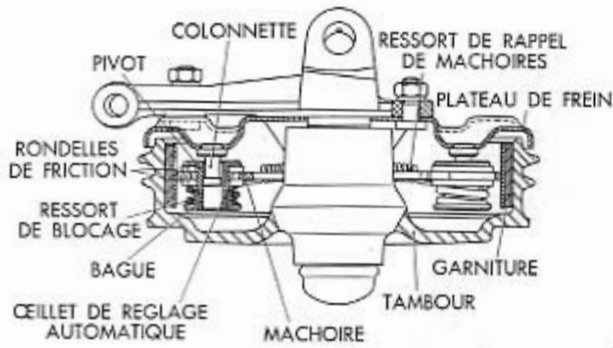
Coupe de l'ensemble freins de la roue avant gauche, sur le dispositif autorégleur.
